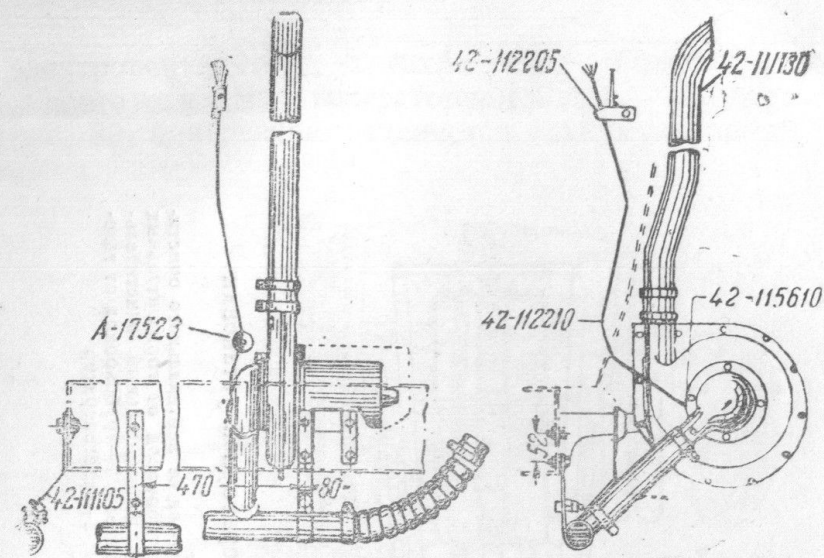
Раздувочный вентилятор и схема крепления трубопроводов
